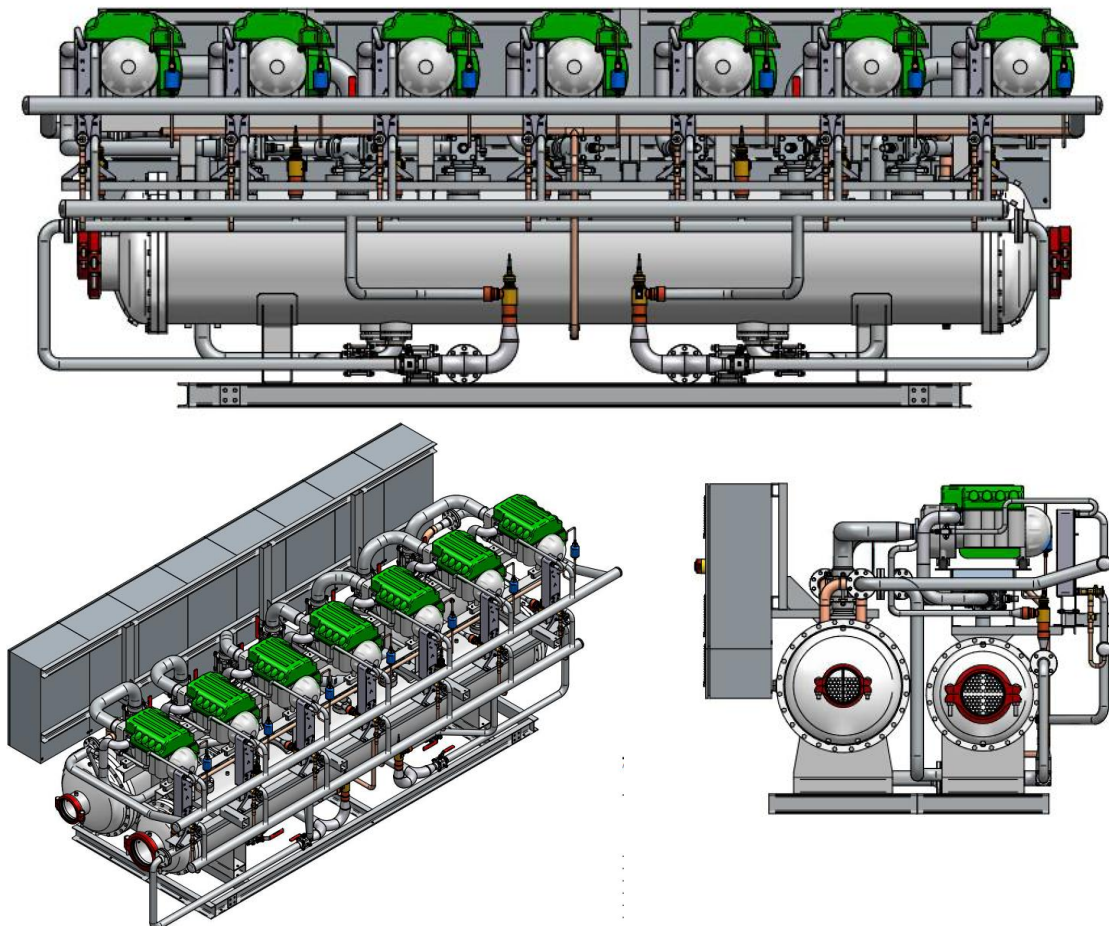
Kältemaschine mit Turbocore-Verdichter „Friotherm AG“ – Technische Zeichnung
